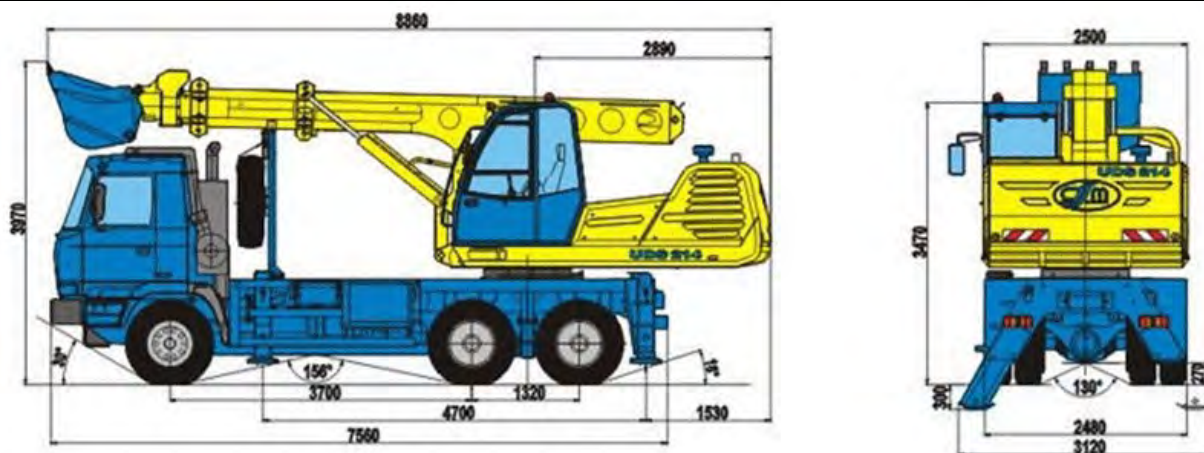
Габаритные размеры экскаватора-планировщика UDS-114а
